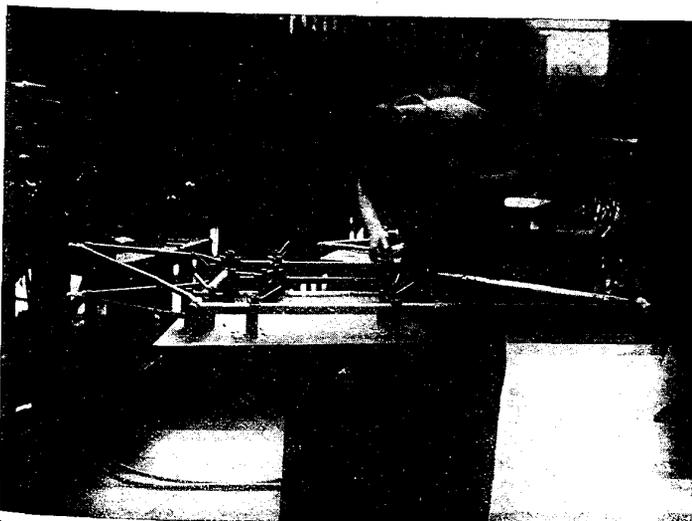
Soudure d'un nœud (1^{re} position)
